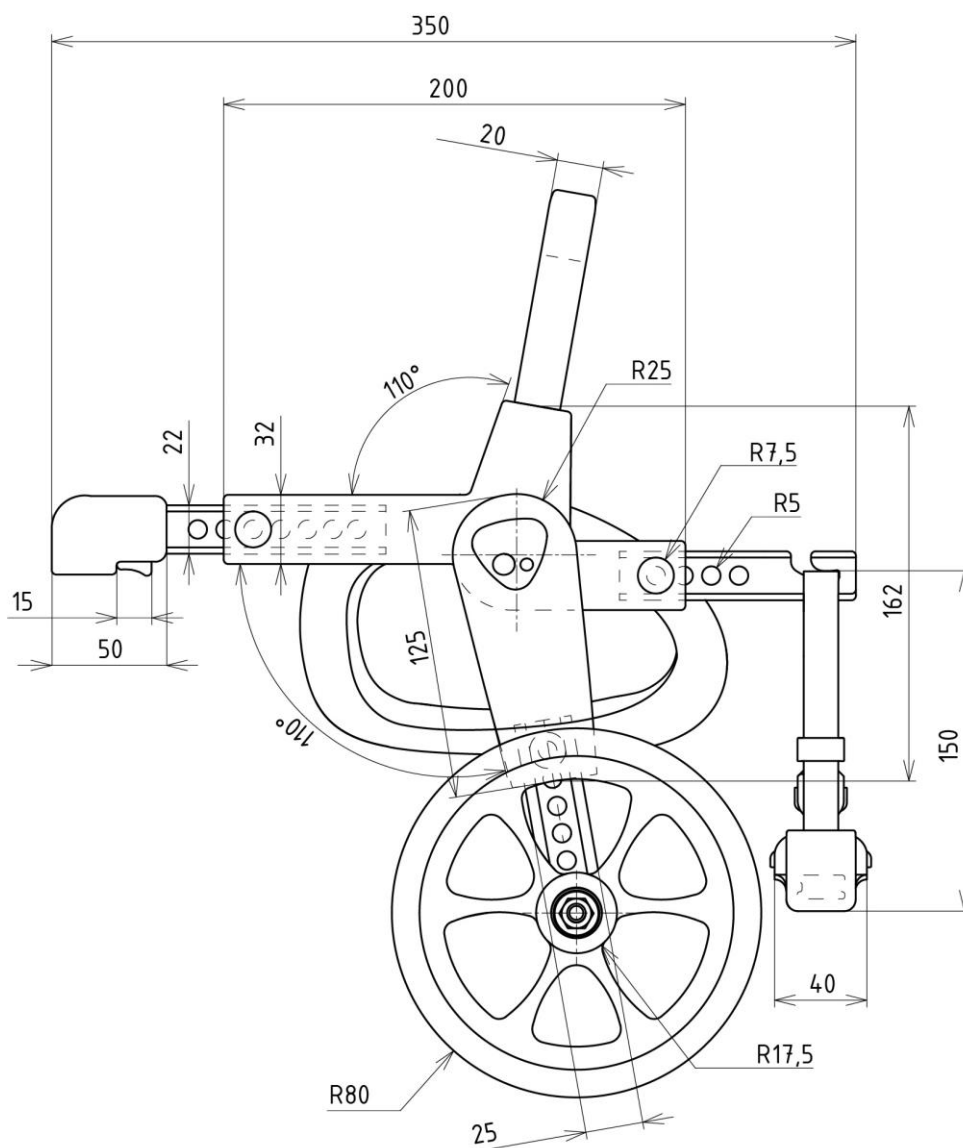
Rozměrové řešení konstrukce – nárys (M 1:3) v mm.
